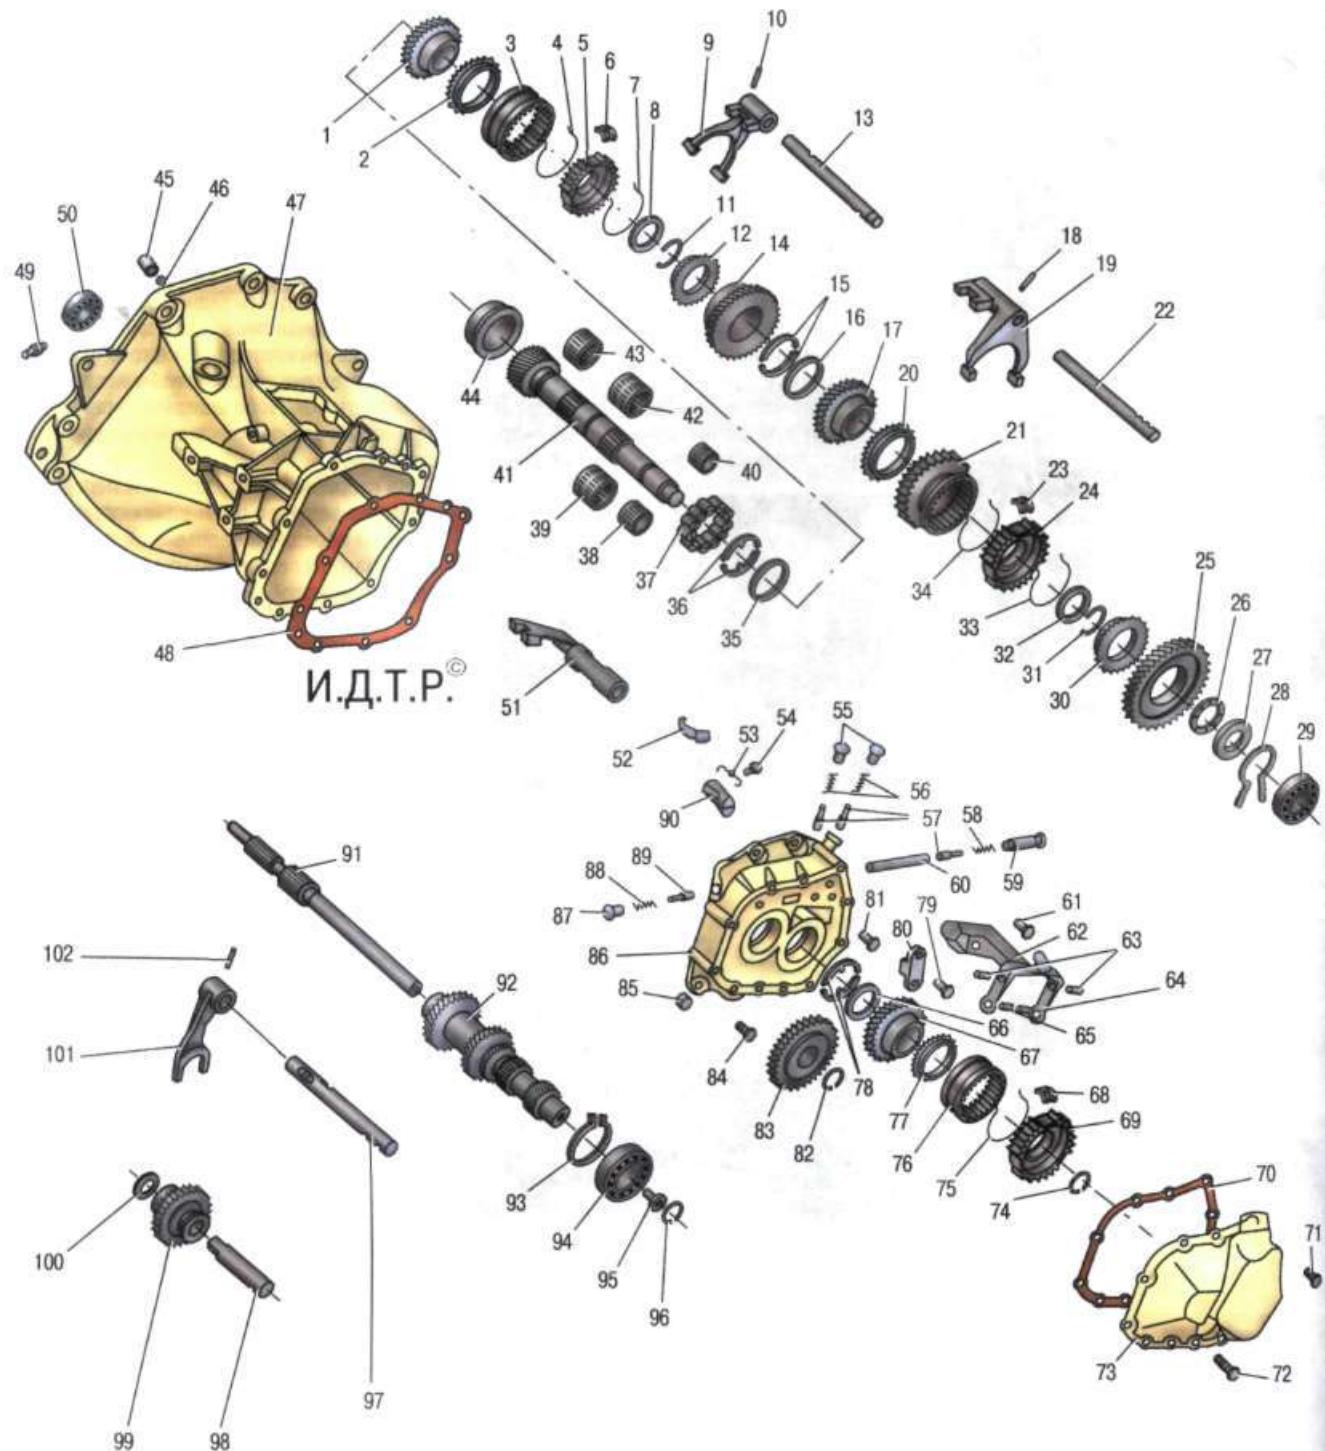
Коробка передач: 1 – шестерня IV передачи; 2, 12, 20, 30, 77 – блокирующие кольца синхронизаторов; 3 – муфта включения синхронизатора III и IV передач; 4, 7, 33, 34, 75 – пружинные кольца синхронизатора; 5 – ступица синхронизатора III и IV передач; 6, 23, 68 – сухари синхронизатора; 8, 32 – упорные шайбы; 9 – вилка переключения III и IV передач; 10, 18, 102 – штифты; 11, 31, 74, 82, 93, 96 – стопорные кольца; 13 – шток вилки переключения III и IV передач; 14 – шестерня III передачи; 15, 36, 78 – упорные полукольца; 16, 35, 66 – запорные кольца; 17 – шестерня II передачи; 19 – вилка переключения I и II передач; 21 – муфта включения синхронизатора I и II передач; 22 – шток вилки переключения I и II передач; 24 – ступица синхронизатора II передач; 25 – шестерня I передачи; 26 – упорный игольчатый подшипник шестерни I передачи; 27 – опорная шайба; 28 – пружинное кольцо; 29 – подшипник вторичного вала; 37 – роликовый подшипник вторичного вала; 38 – игольчатый подшипник шестерни I передачи; 39 – игольчатый подшипник шестерни II передачи; 40 – игольчатый подшипник шестерни V передачи; 41 – вторичный вал; 42 – игольчатый подшипник шестерни III передачи; 43 – игольчатый подшипник шестерни IV передачи; 44 – наружное кольцо роликового подшипника вторичного вала; 45 – пробка; 46 – магнит; 47 – картер коробки передач; 48 – прокладка картера коробки передач; 49 – выключатель фонарей света заднего хода; 50 – роликовый подшипник первичного вала; 51 – поводок соленком V передачи; 52 – собака; 53 – пружина собаки; 54, 61, 71, 72, 79, 81, 84 – болты; 55, 59, 87 – пробки фиксаторов; 56, 58, 88 – пружины; 57, 89 – фиксаторы; 60 – штифт механизма блокировки; 62 – кронштейн вилки включения V передачи; 63 – ось вилки включения V передачи; 64 – вилка включения V передачи; 65 – сухари вилки; 67 – ведомая шестерня V передачи; 69 – ступица синхронизатора V передачи; 70 – прокладка крышки; 73 – крышка коробки передач; 76 – муфта включения синхронизатора V передачи; 80 – кронштейн собаки; 83 – ведущая шестерня V передачи; 85 – магнит; 86 – промежуточные картеры; 90 – кронштейн собаки; 91 – первичный вал; 92 – блок шестерен; 94 – шариковый подшипник блока шестерен; 95 – винт; 97 – шток вилки включения промежуточной шестерни заднего хода; 98 – ось промежуточной шестерни заднего хода; 99 – промежуточная шестерня заднего хода; 100 – вилка включения промежуточной шестерни заднего хода.
